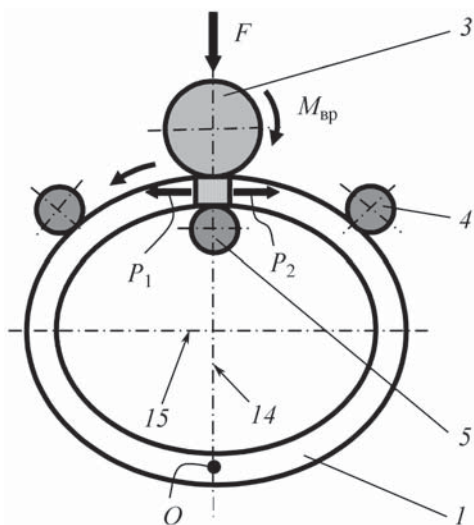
Промежуточный этап калибровки раскатываемой и кольцевой заготовки
